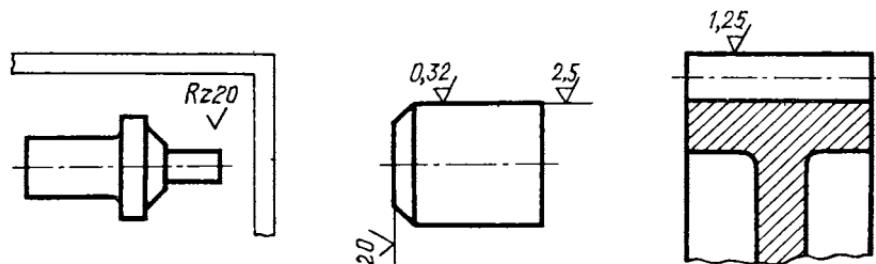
Примеры обозначения шероховатости поверхности на чертежах.
